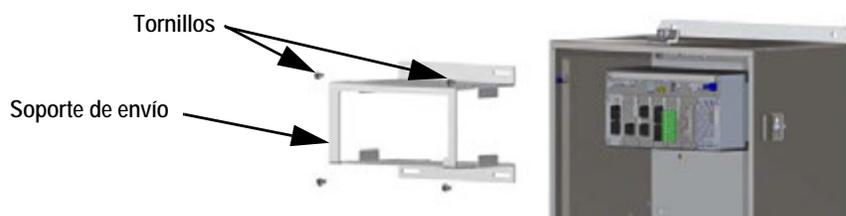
Extracción del soporte de envío - Montaje en pared
